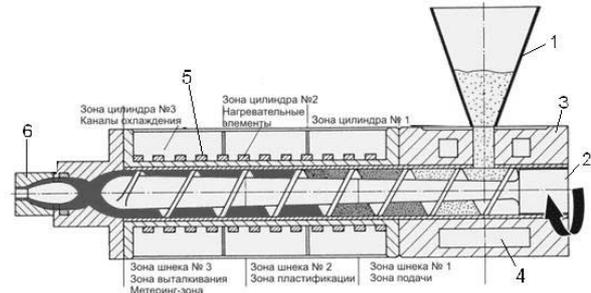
Устройство экструдера: 1 – бункер; 2 – шнек; 3 – цилиндр; 4 – полость для воды; 5 – нагреватель; 6 – формующая головка
